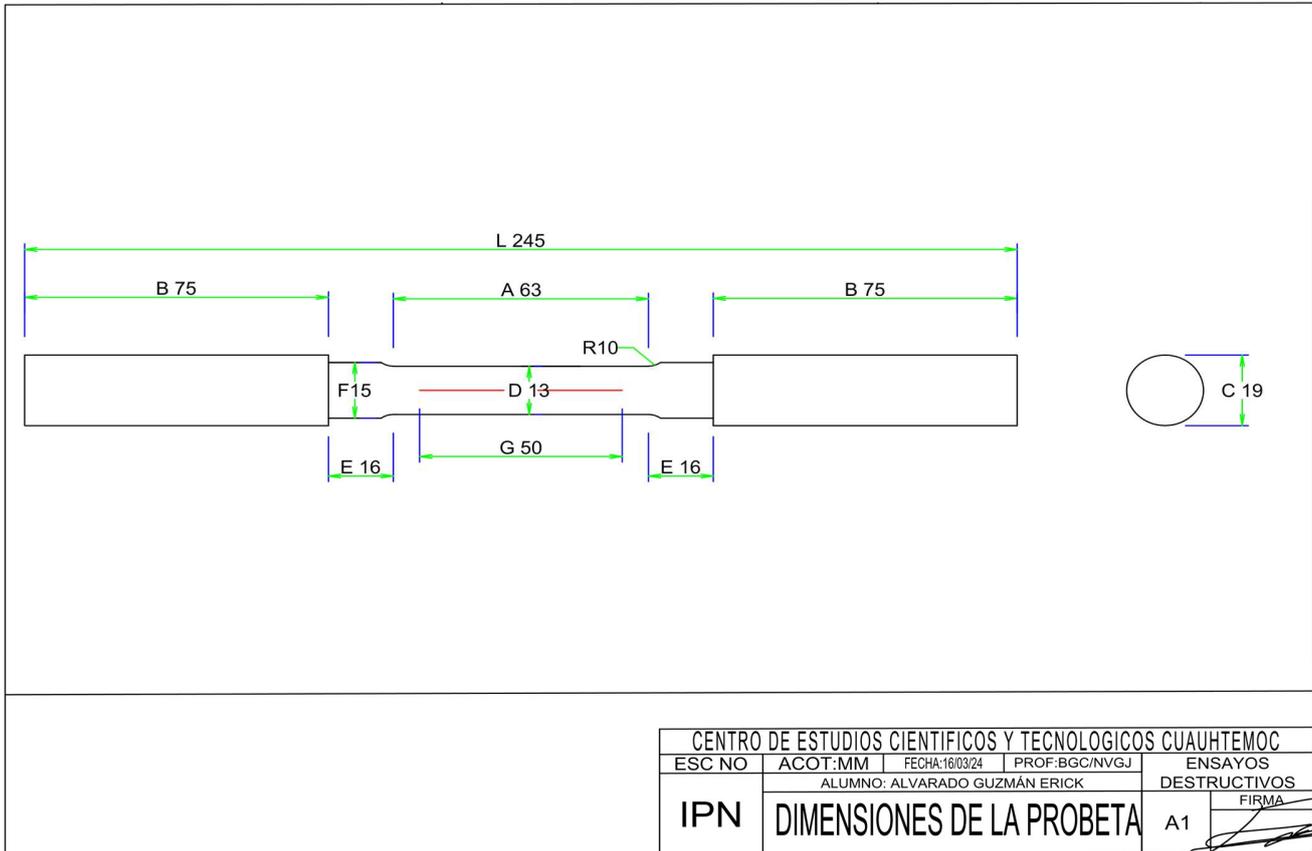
Dimensiones en la probeta de acero (en milímetros)
